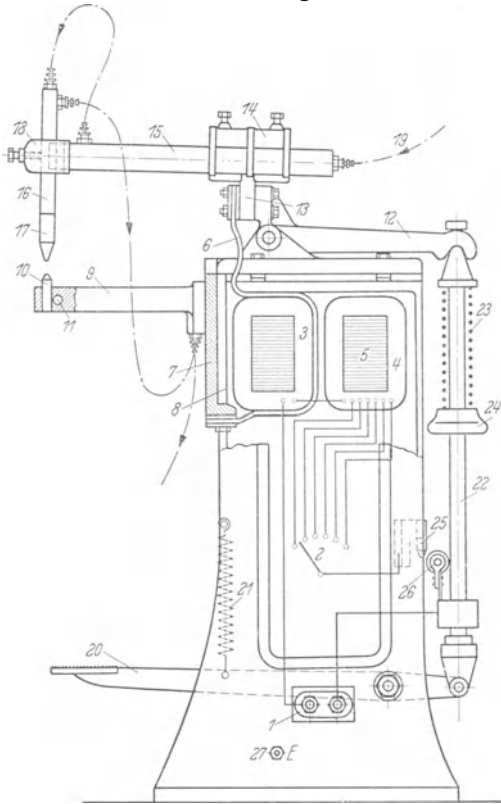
Aufbau einer Punktschweißmaschine.
